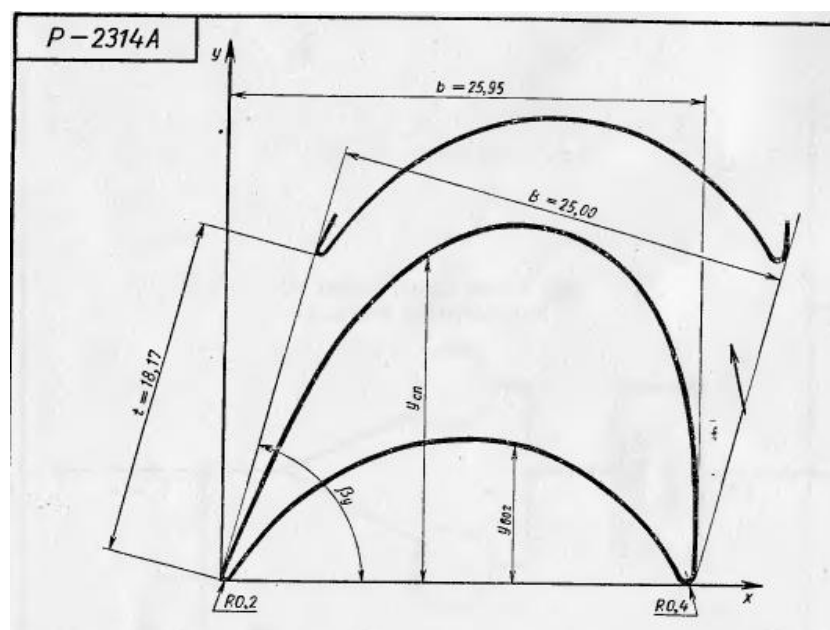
Профиль рабочей решетки Р-23-14А
